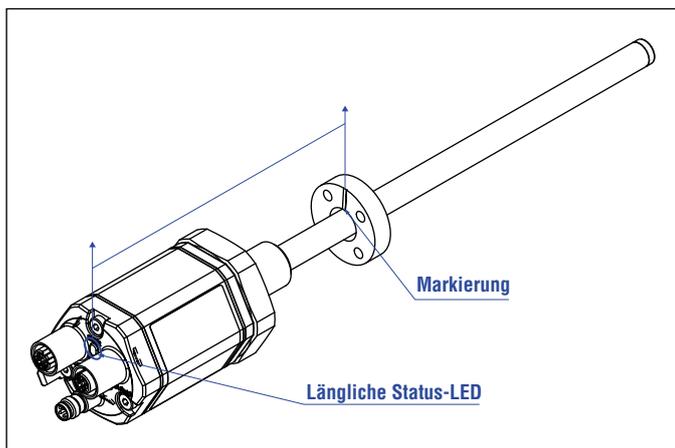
Magnetausrichtung mit Ringmagnet für RH5 EtherCAT® mit interner Linearisierung
